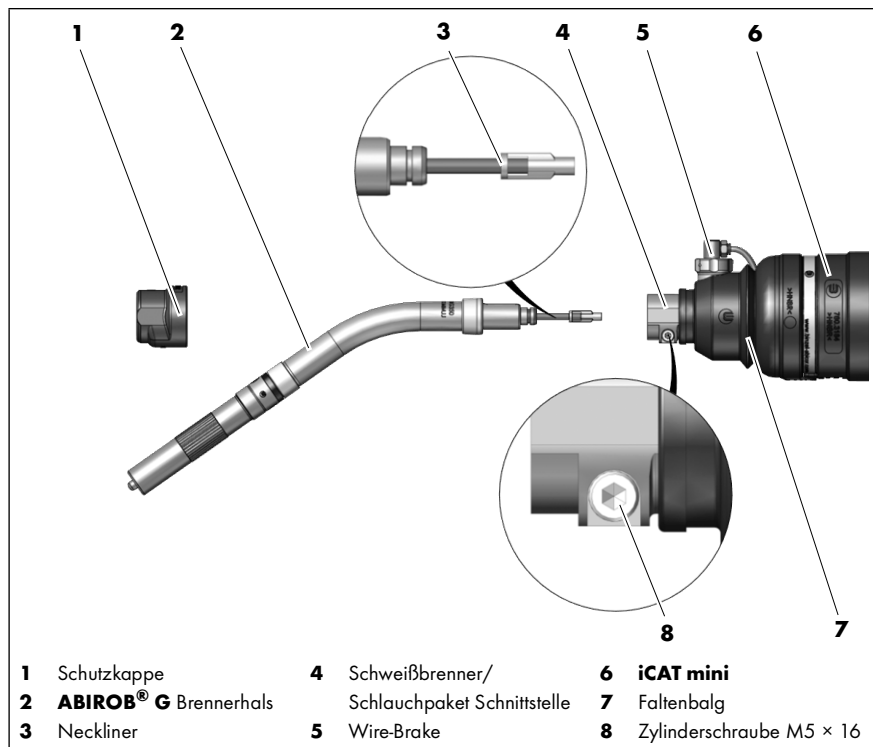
Schweißbrennerhals ABIROB® G befestigen (iCAT mini mit Wire-Brake)
